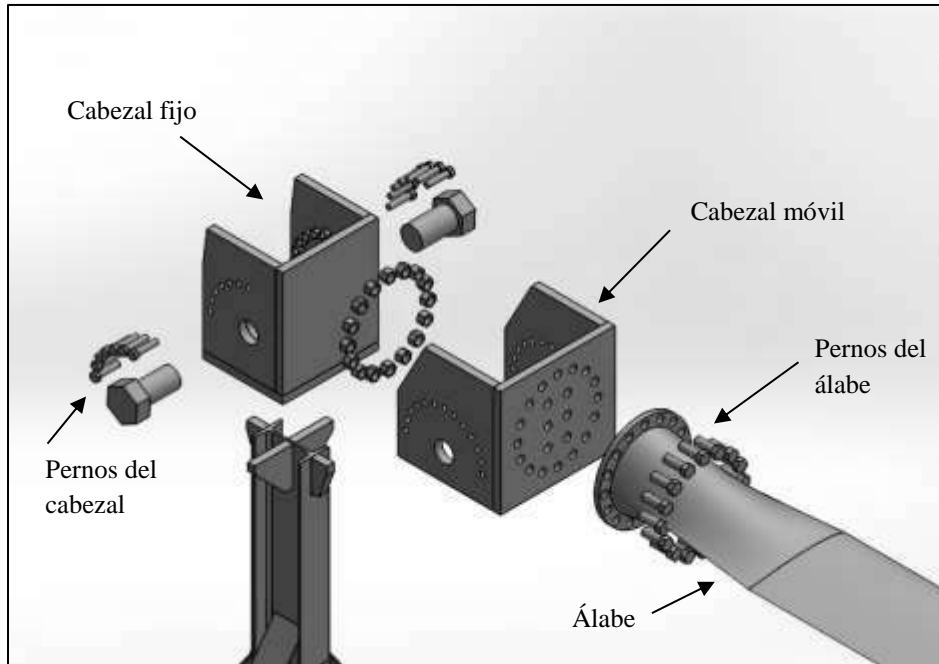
Vista explosionada del cabezal 2. Fuente: SOLIDWORKS 2017.
